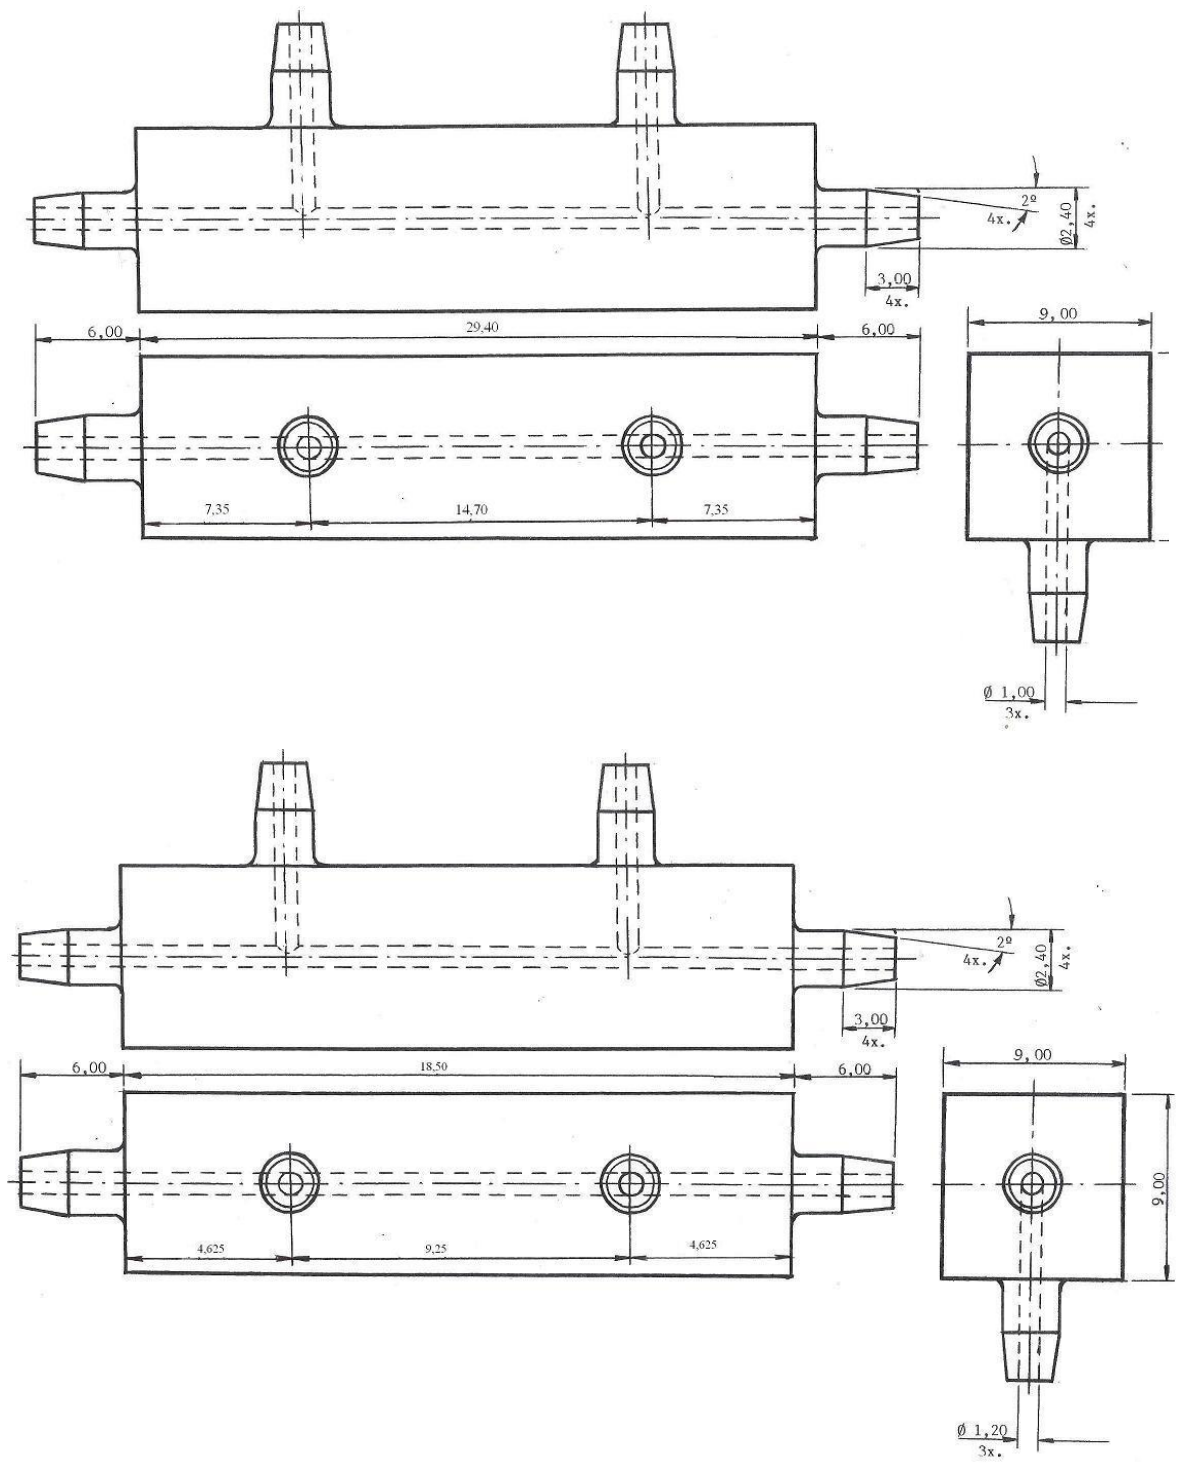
Desenho dos pneumotacógrafos inspiratório (painel superior) e expiratório (painel inferior). Dimensões em mm.
